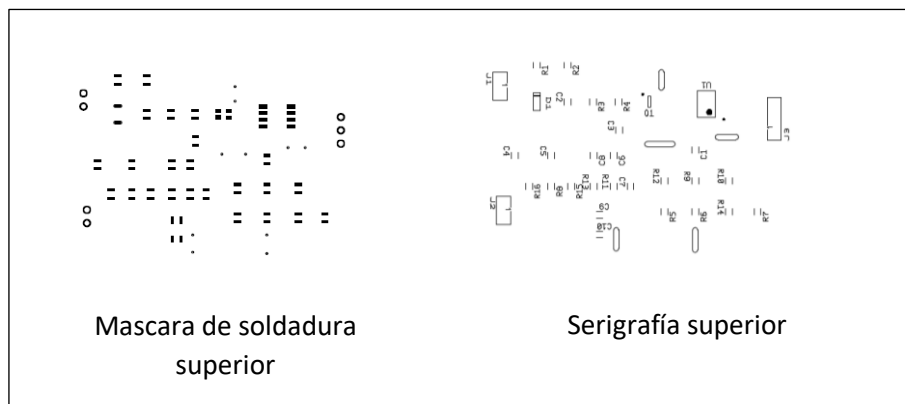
Diseño de mascara de soldadura y serigrafía superior.
